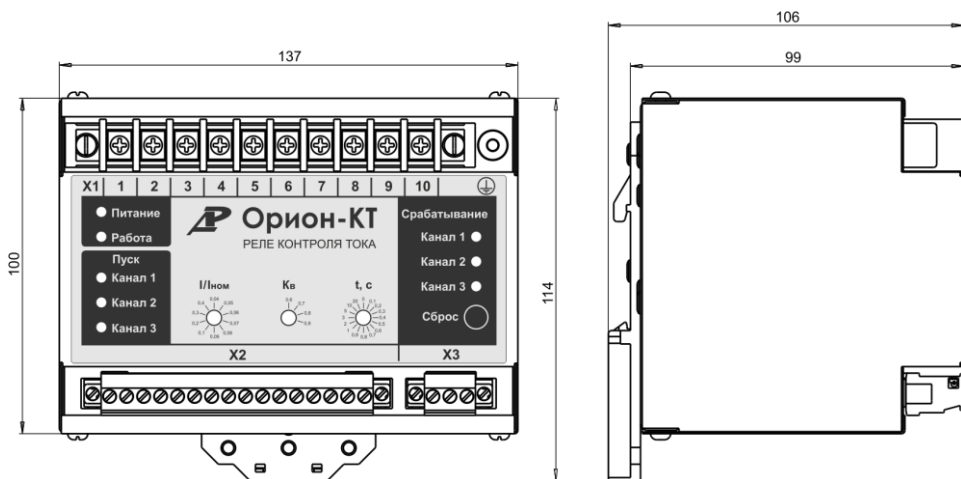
Внешний вид и габаритные размеры устройства «Орион-КТ»
